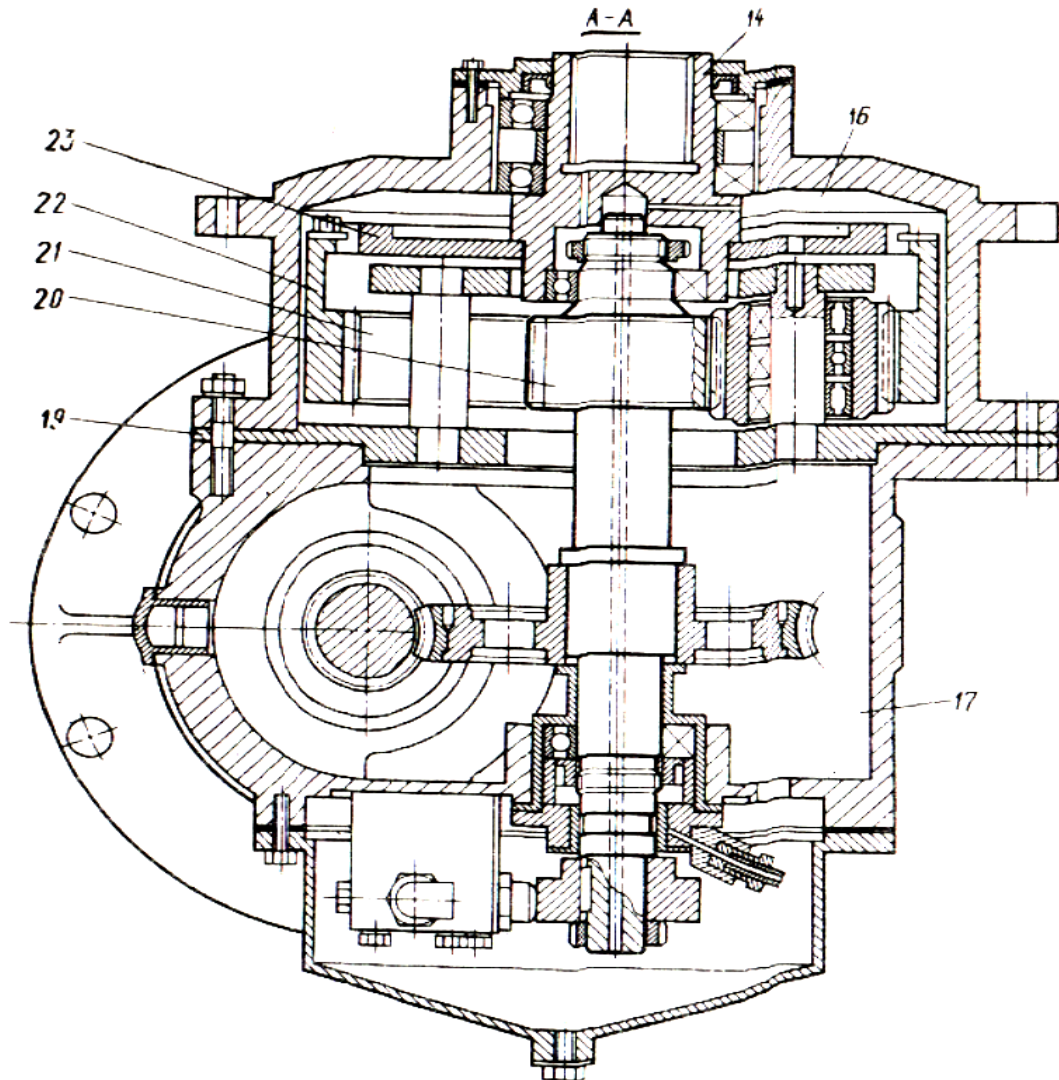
Однопалубний якірно-швартовний шпиль
